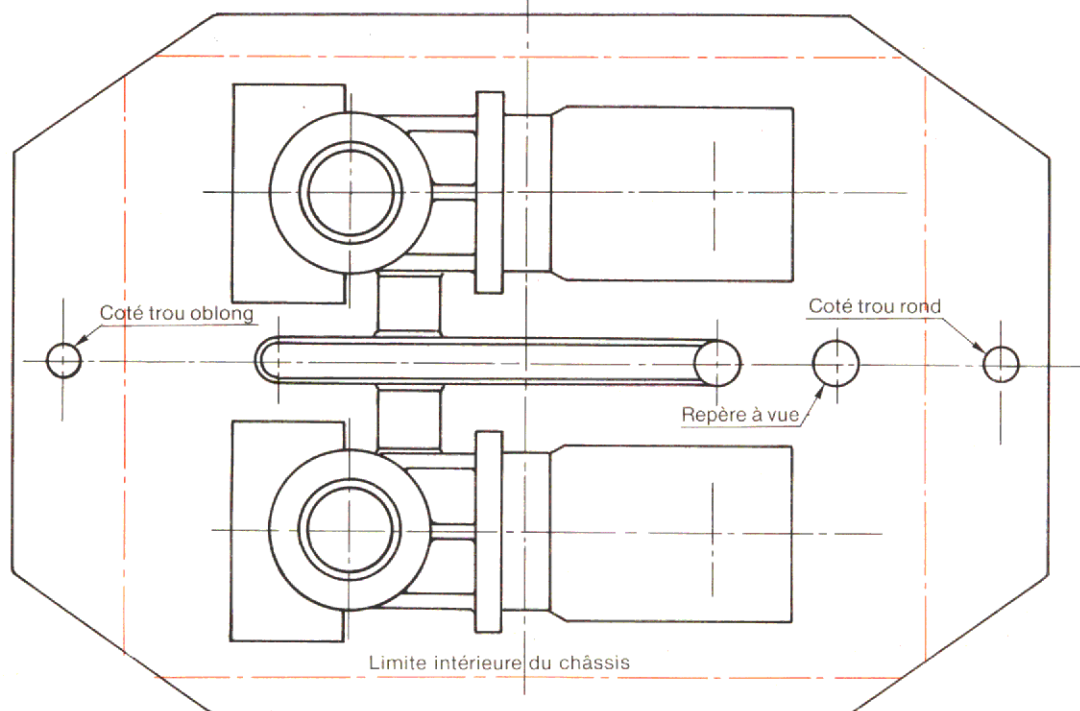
Plaque modèle pour châssis de dessus.
